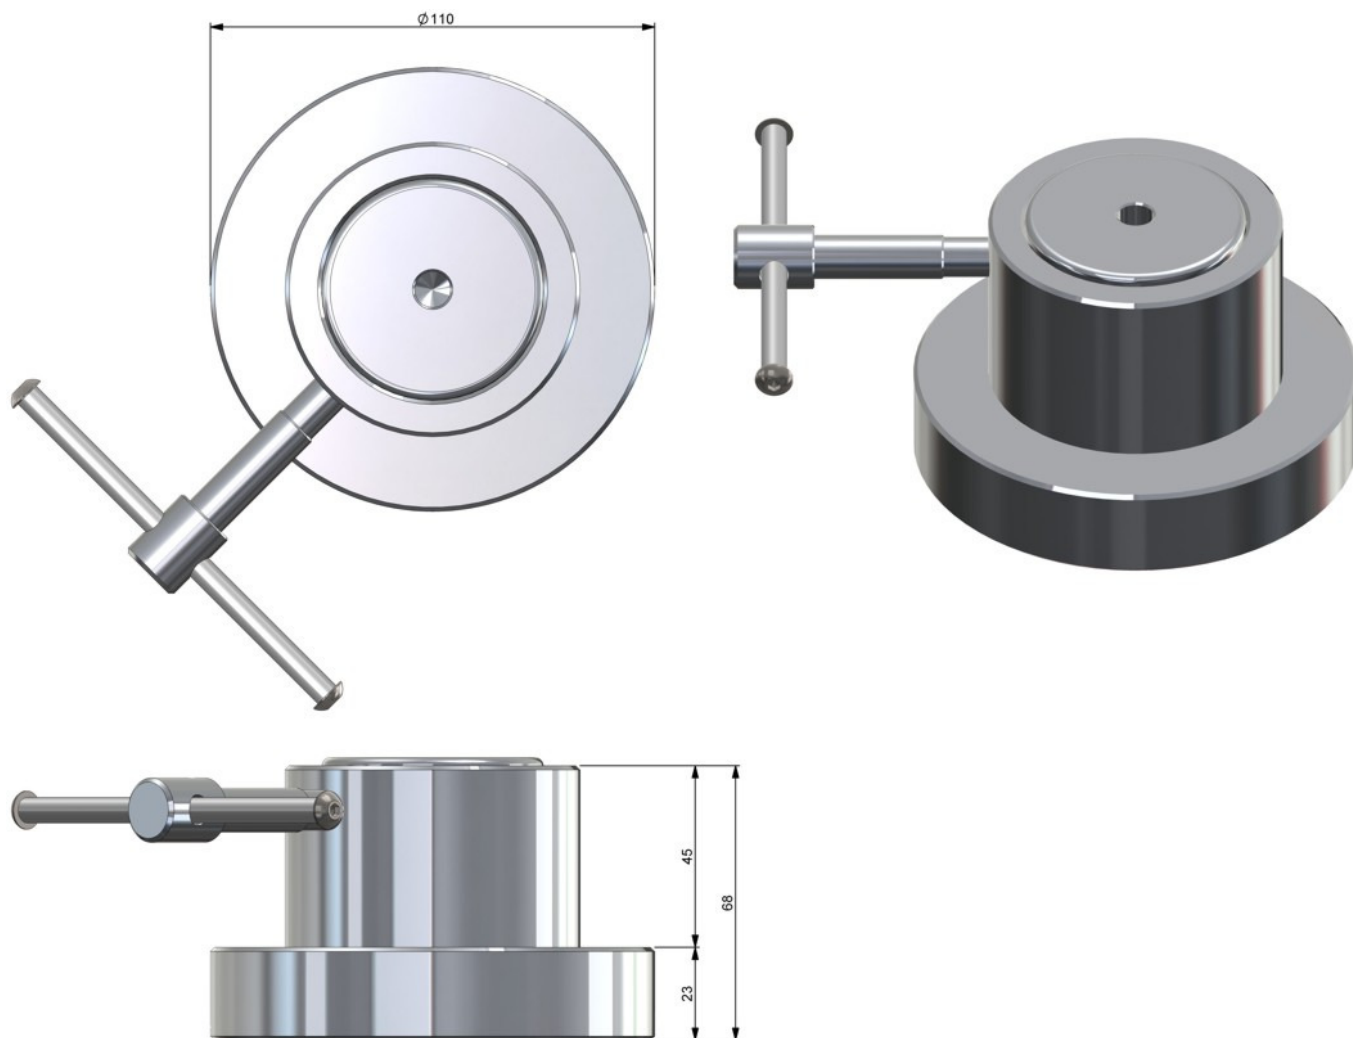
Dimensionamento para montagem da Flange (Cotas em milímetro)
